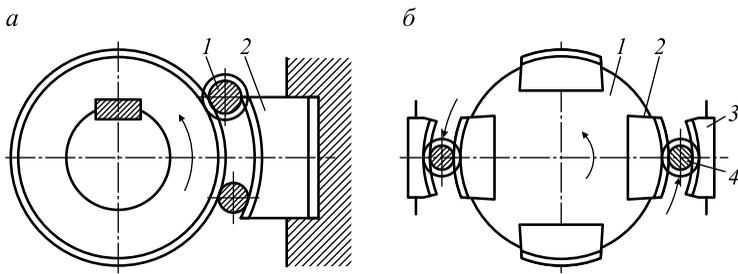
Схема накатывания резьбы сегментными шпонками
